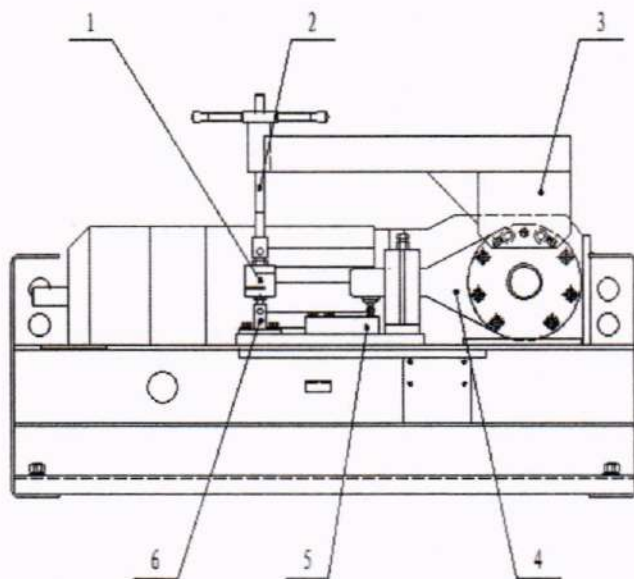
Устройство для калибровки датчиков тормозного усилия: 1 – эталонный динамометр, 2 – загрузочный винт, 3 – калибровочный рычаг, 4 – рычаг, 5 – тензометрический датчик, 6 – наконечник
